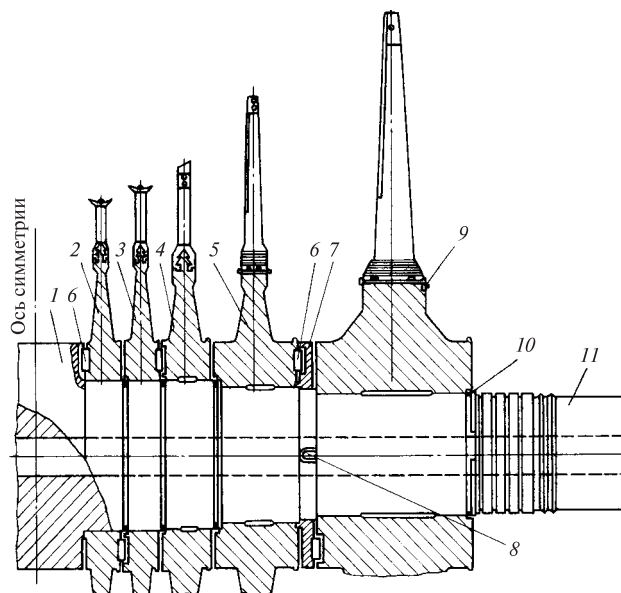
Сборный ротор двухпоточного ЦНД турбины ХТЗ: 1 — выступ вала; 2 — 5 — диски первой — четвертой ступеней; 6 — торцевая шпонка; 7 — шпоночное кольцо; 8 — осевая шпонка; 9 — балансировочный груз; 10 — кольцо для осевой фиксации диска; 11 — шейка вала под вкладыш подшипника
